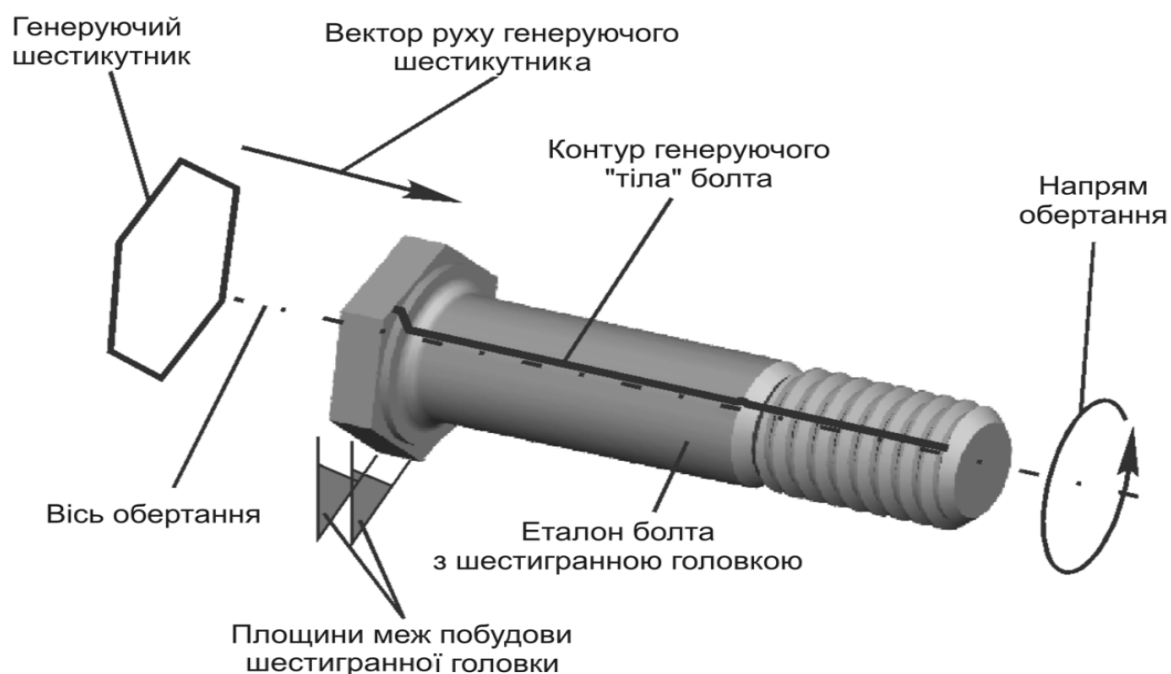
Побудова аналітичного еталона болта з шестигранною головкою
